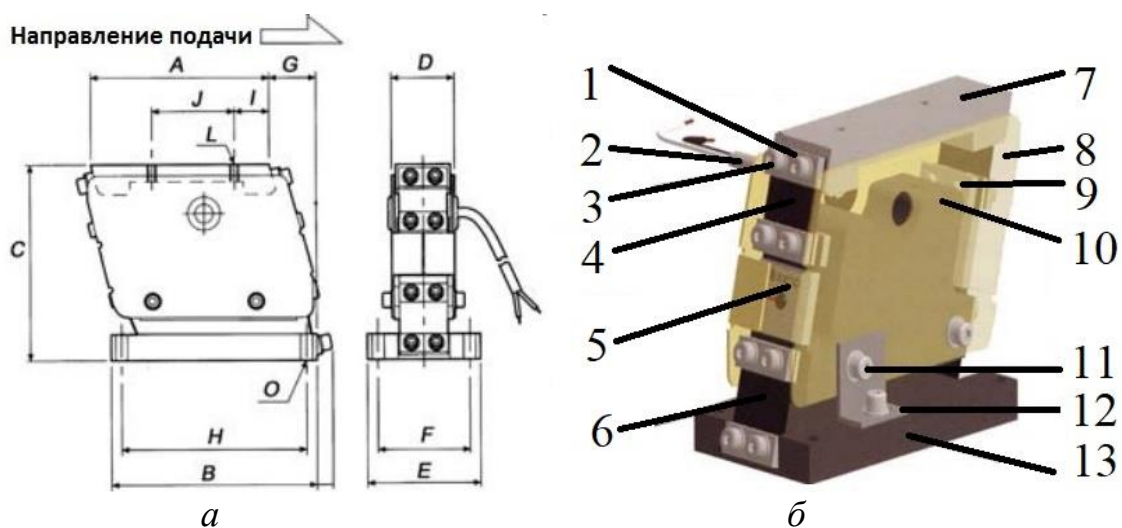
Схематическое изображение линейного пьезоэлектрического вибрационного привода L60A: 1 – крепление пружины; 2 – провода; 3 – болт; 4 – пластичная пружина; 5 – пьезорезонатор; 6 – пластинчатая пружина; 7 – рабочий стол; 8 – крышка; 9 – фиксатор пьезорезонатора; 10 – противовес; 11 – болт скобы; 12 – транспортная скоба; 13 – основание
